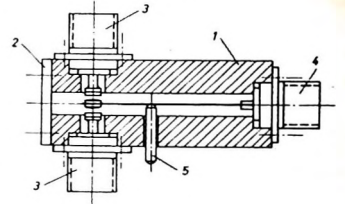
Schnittzeichnung des Koaxialumschalters Ausführung A, Kontaktfeder noch nicht justiert
